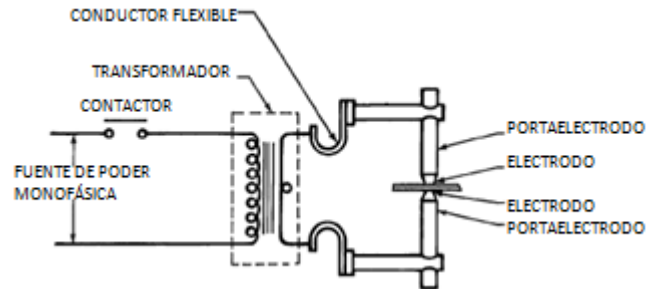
Diagrama típico de un circuito de Soldadura por Puntos monofásico [5].
